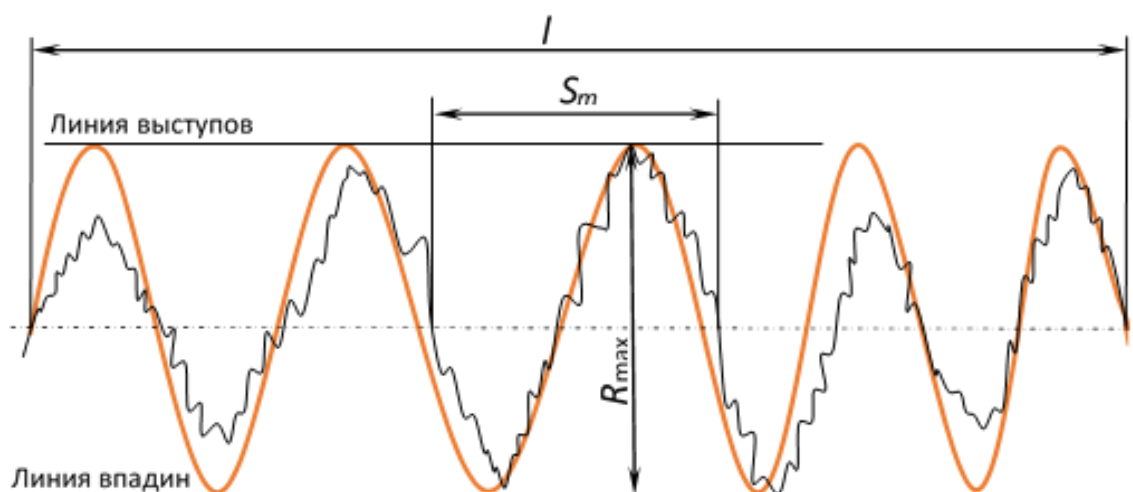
Параметры шероховатости опорной поверхности газостатической опоры
